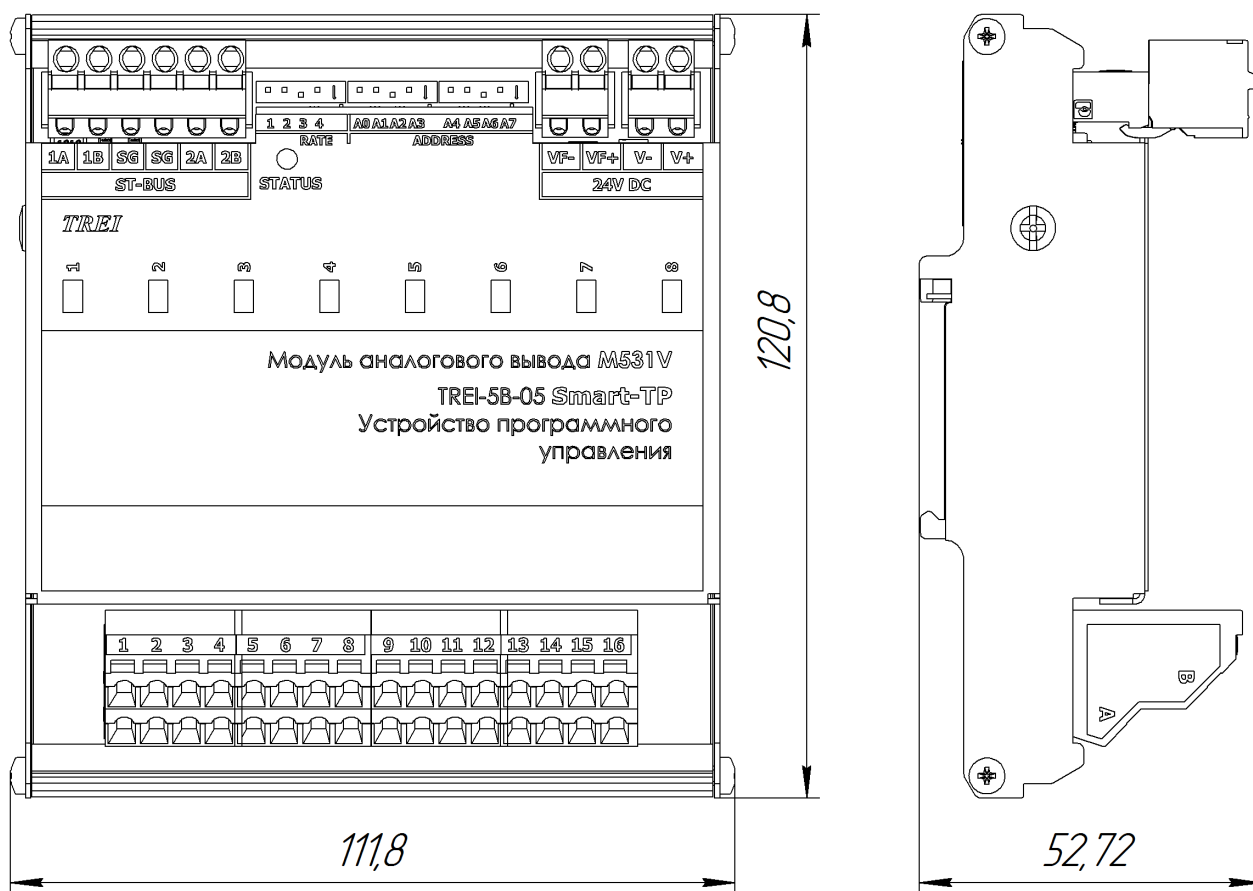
Чертеж общего вида M531V с указанием габаритных и присоединительных размеров
